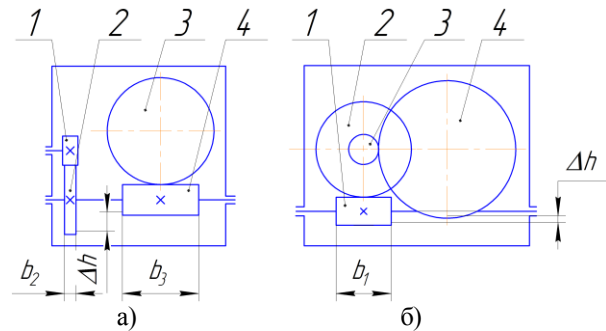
Схемы цилиндрично-червячного (а) и червячно-цилиндрического редукторов (б)
